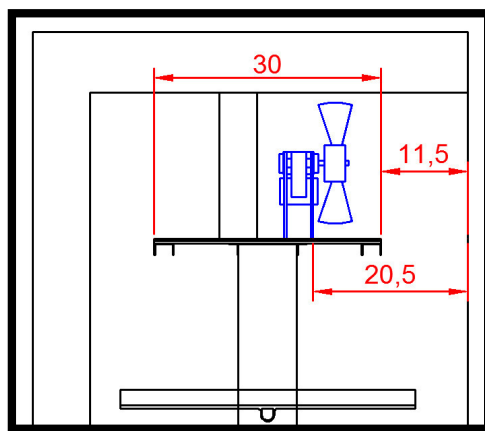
Vista lateral de las medidas para la colocación de ventilador de flujo de calor. Elaboración: Los autores
